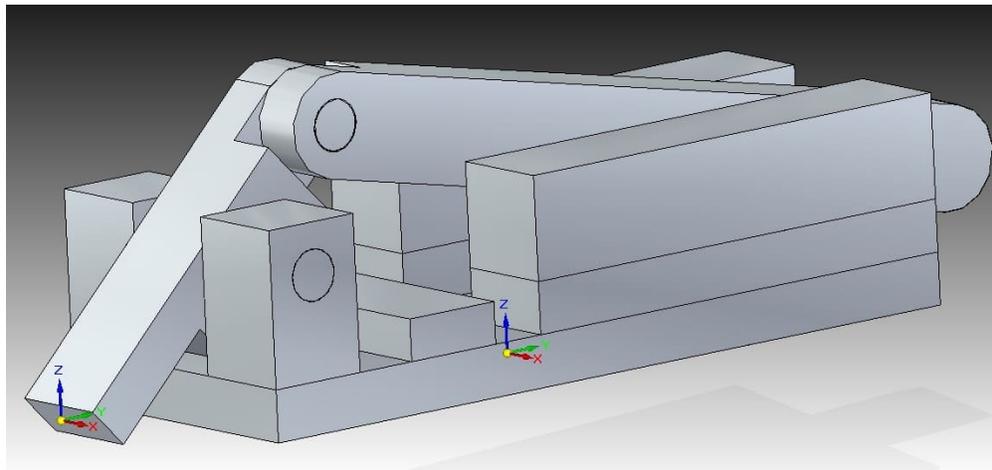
CAD del mecanismo de la tapa inferior de prensado
